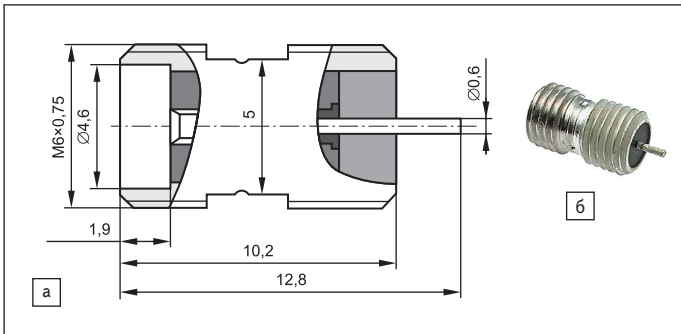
Соединитель CPГ50-751ФВ: а) конструкция; б) внешний вид
